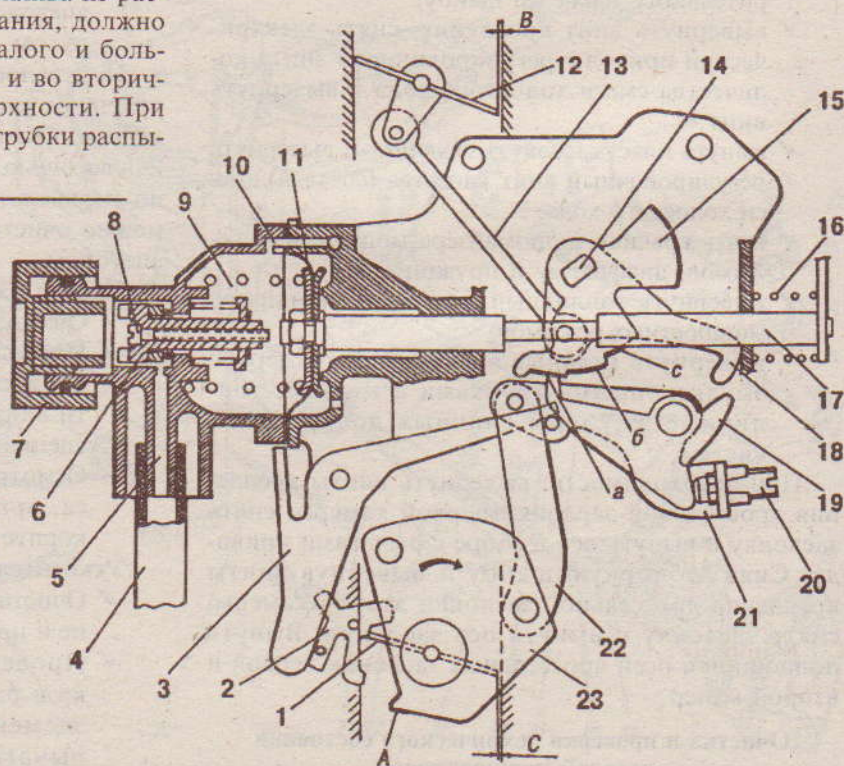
Схема пускового устройства карбюратора: 1 - дроссельная заслонка первой камеры; 2 - рычаг блокировки второй камеры; 3 - рычаг привода блокировки; 4 - шланг к ресиверу; 5 - штуцер; 6 - плунжер; 7 - упор регулировки второй ступени; 8 - регулировочный винт; 9 - диафрагменная полость; 10 - воздушный канал из задроссельного пространства карбюратора; 11 - диафрагма пускового устройства; 12 - воздушная заслонка; 13 - тяга привода воздушной заслонки; 14 - ось пускового устройства; 15 - кулачок; 16 - пружина штока; 17 - шток диафрагмы пускового устройства; 18 - крючок блокировки второй камеры; 19 - рычаг упора; 20 - регулировочный винт приоткрывания дроссельной заслонки первой камеры; 21 - рычаг приоткрывания дроссельной заслонки; 22 - тяга приоткрывания дроссельной заслонки; 23 - рычаг управления дроссельными заслонками; А - упор блокировки второй камеры; В - пусковой зазор у воздушной заслонки; С - пусковой зазор у дроссельной заслонки; а, б, с - первая, вторая и третья ступени кулачка
